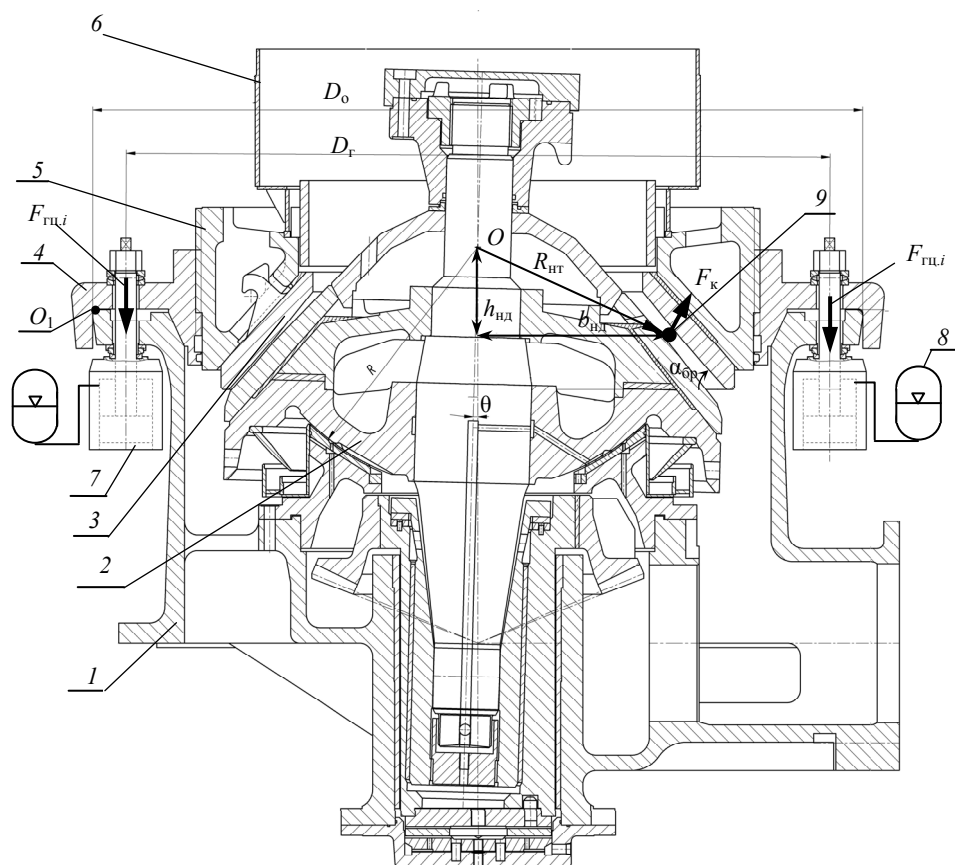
Схема для расчета параметров: 1 – корпус дробилки; 2 – конус; 3 – броня чаши; 4 – кольцо опорное; 5 – кольцо регулирующее; 6 – загрузочная часть; 7 – гидроцилиндры; 8 – гидропневмоаккумуляторы; 9 – недробимое тело; $D_{оп}$ – диаметр опорного кольца; $D_{гц}$ – диаметр расположения штоков гидроцилиндров; $R_{нт}$ – радиус от точки подвеса до недробимого тела; O – условная точка подвеса (центр кривизны опорной поверхности конуса); O_1 – точка поворота кольца опорного; $F_{гц,i}$ – усилие на i -м штоке гидроцилиндра; $F_к$ – усилие, передаваемое через недробимое тело от конуса на броню чаши; γ – угол нутации
